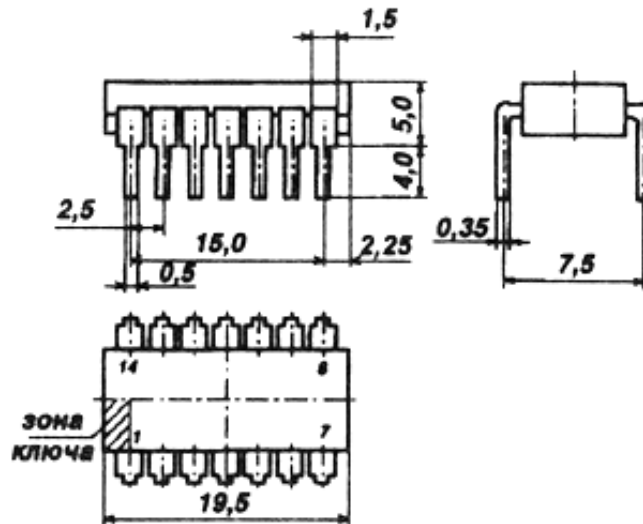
Креслення корпусу ІМС К561ЛА7
